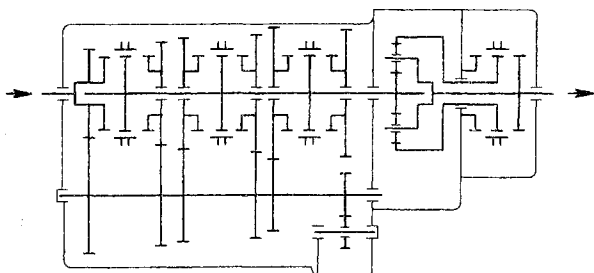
Кинематическая схема девятиступенчатой коробки передач ЯМЗ-202
